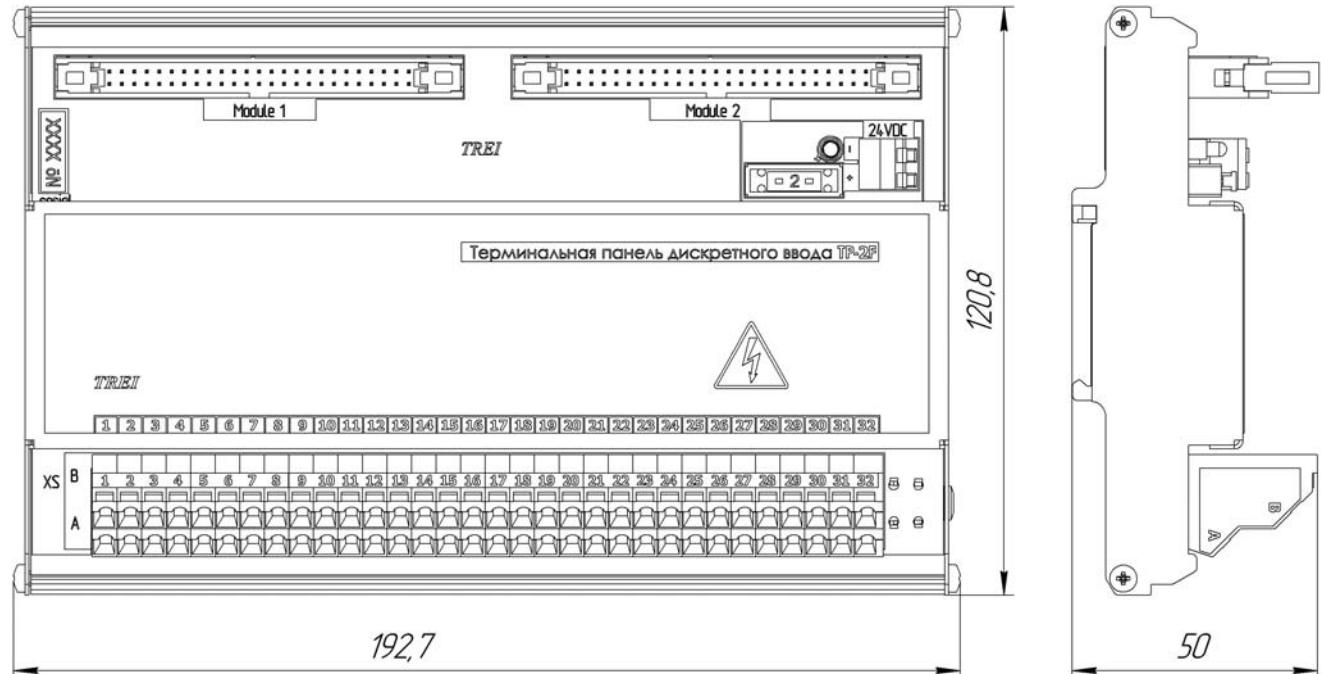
Чертеж общего вида ТР-2F с указанием габаритных размеров
